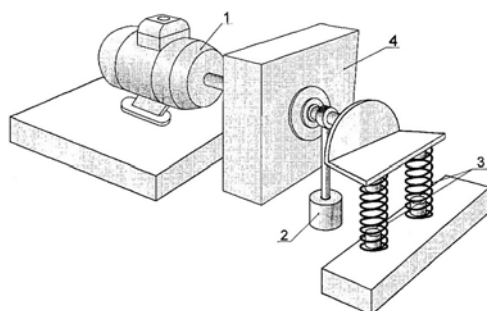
Автоколебательный стенд для испытания пружин асинхронный электродвигатель (1), понижающий редуктор на цилиндрических шестернях (4), компенсатор реактивной механической энергии в виде маятника (2) или испытываемых пружин (3)
